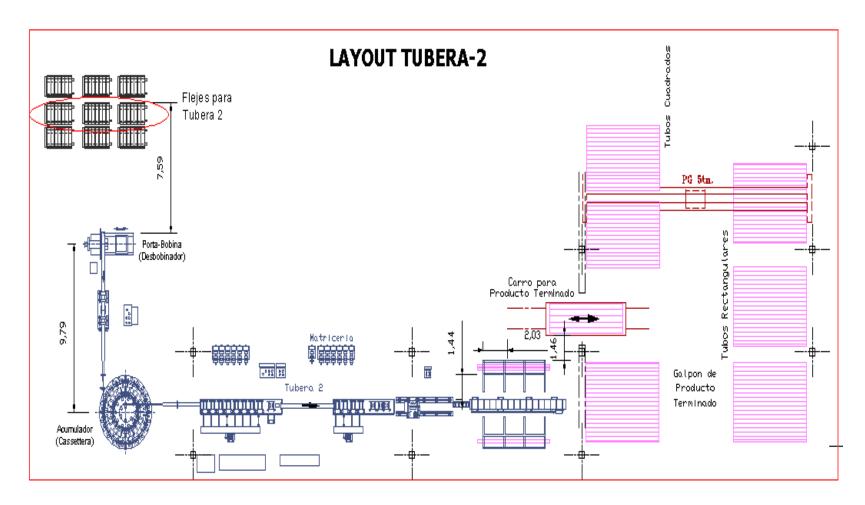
LAYOUT DE LA TUBERA 2
